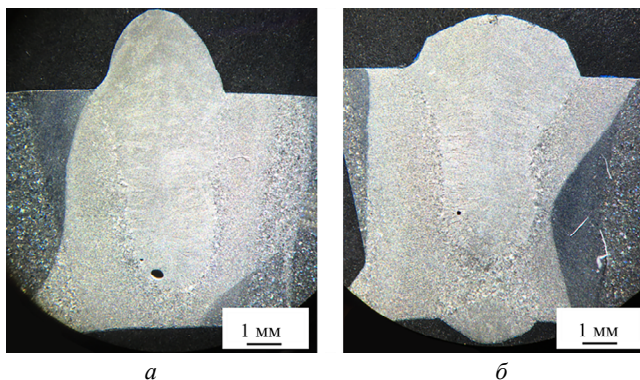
Микрофотографии поперечного сечения наплавленного металла:
